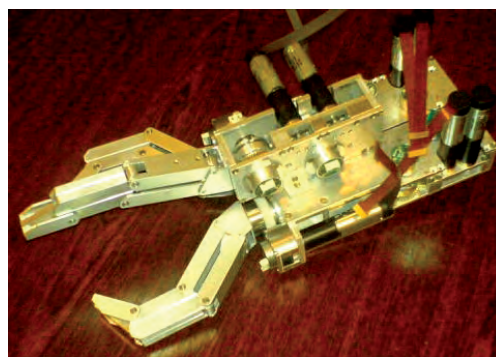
Rozwiązanie konstrukcyjne mechanizmu palca obrotowego typu kciuk
